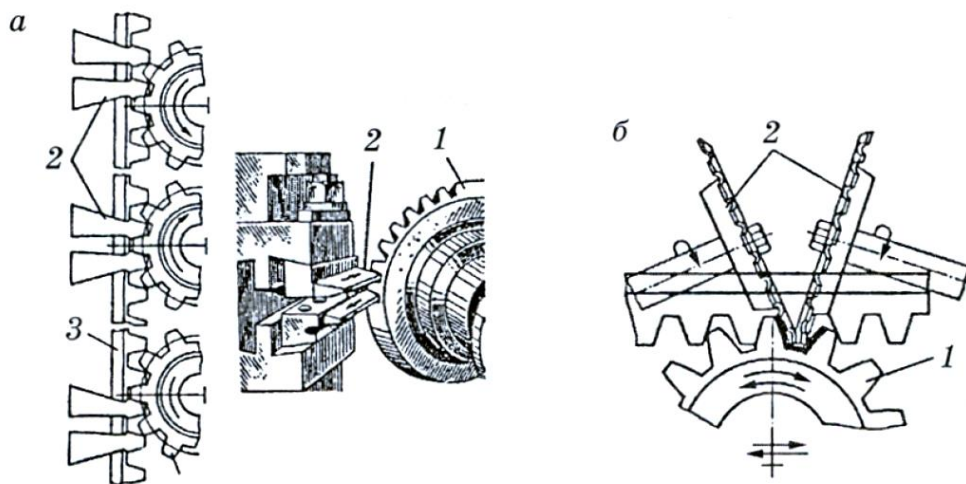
Нарезание зубьев конических зубчатых колес: а – зубострогание двумя резцами; б – фрезерование двумя дисковыми фрезами; 1 – обрабатываемое зубчатое колесо; 2 – режущий инструмент; 3 – плоский венец
